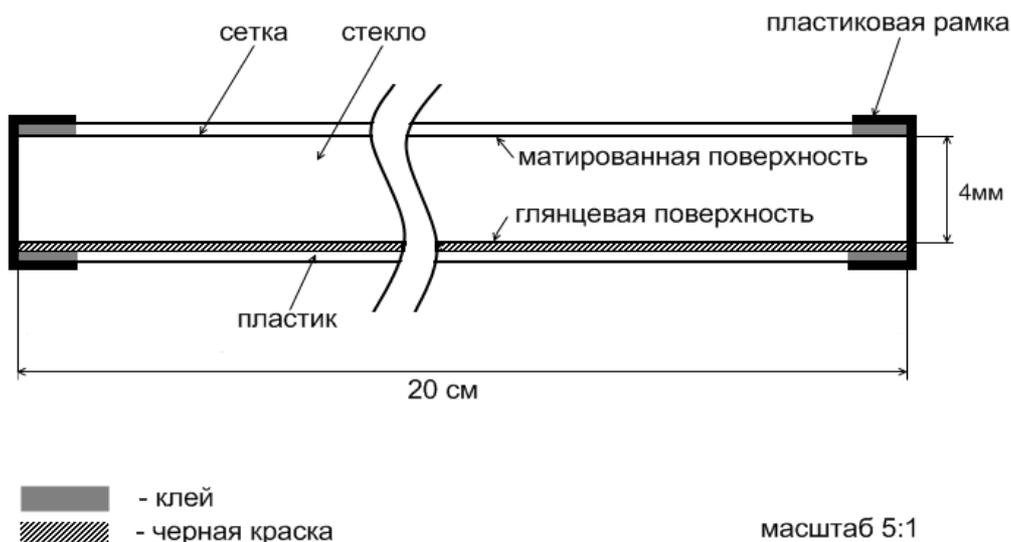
Конструкция опытного экземпляра калибровочного стандарта
